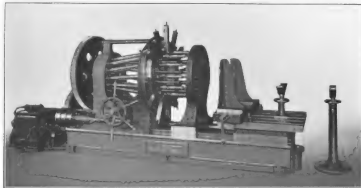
Mehrspindelige Horizontal-Bohrmaschine von Habersang & Zinnen in Düsseldorf-Oberbilk.
